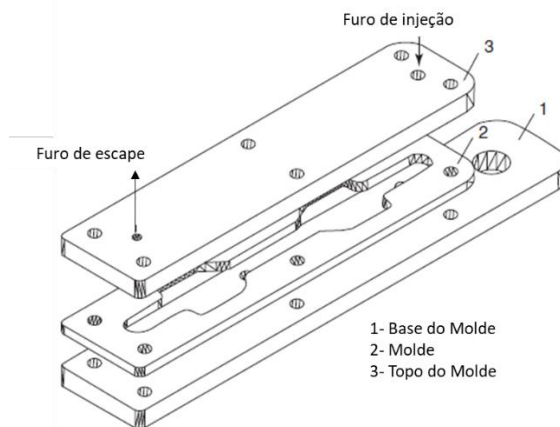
Representação esquemática de um molde utilizado para o fabrico de provetes *bulk* [18].
